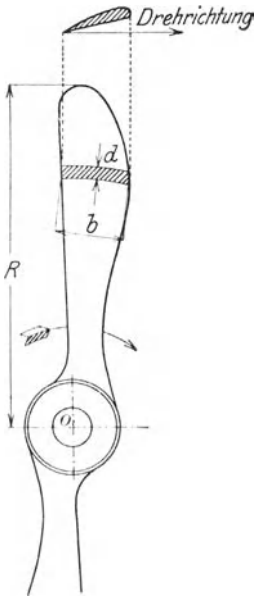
Ansicht u. Querschnitt einer Luftschraube.
